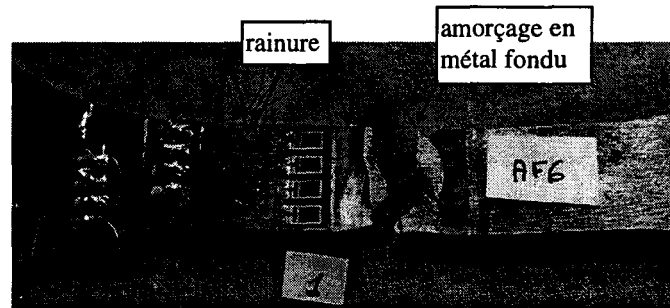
Exemple de fissuration dans le métal fondu sur une éprouvette AR (AF6)
